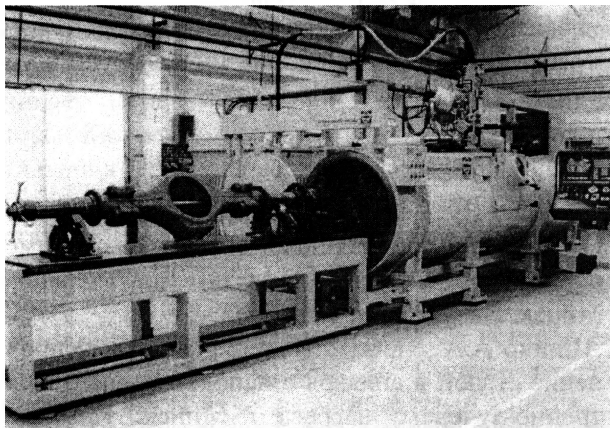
Установка для ЭЛС корпуса моста грузового автомобиля
